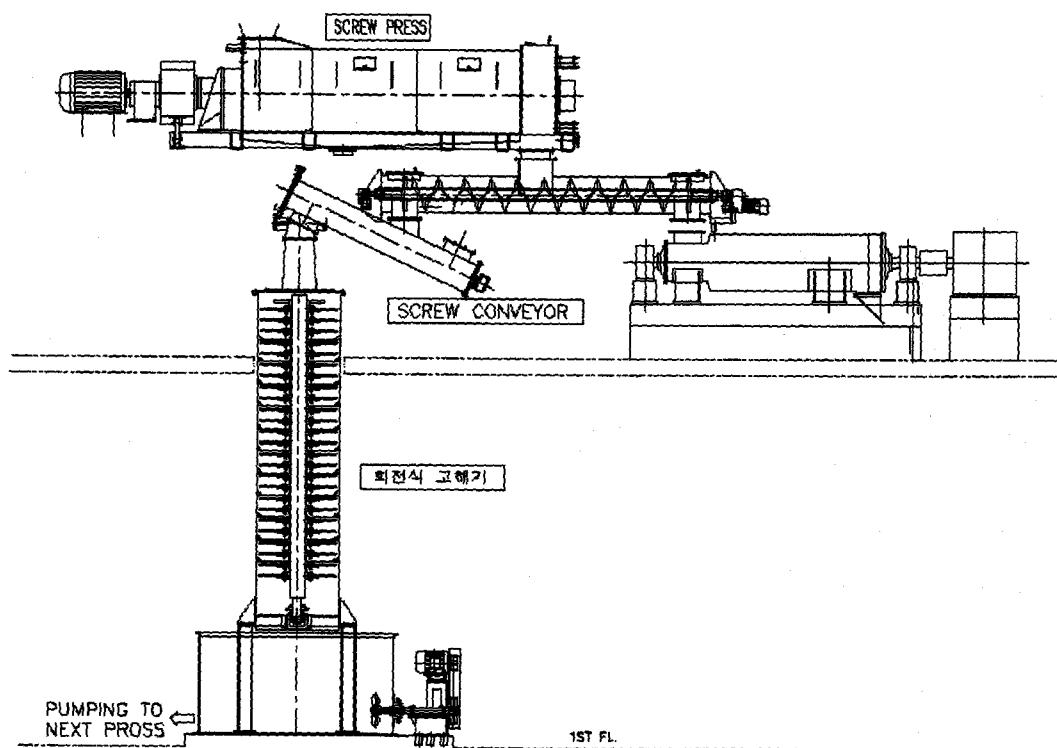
신설 screw conveyor 및 CAT 설치도.
